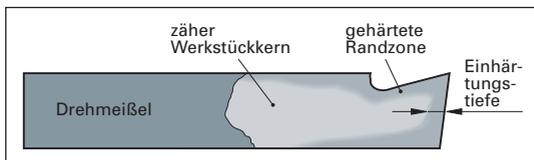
Eindhärtungstiefe an einem Drehmeißel aus unlegiertem Werkzeugstahl
